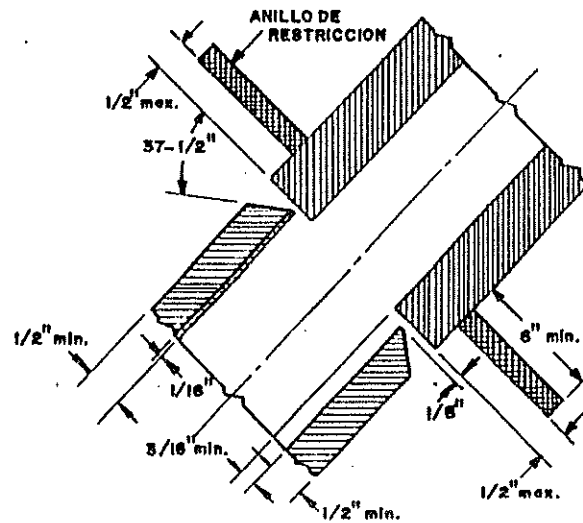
Localización de ensayos para soldadura de tubería redonda y cuadrada para calificación de soldadores.
